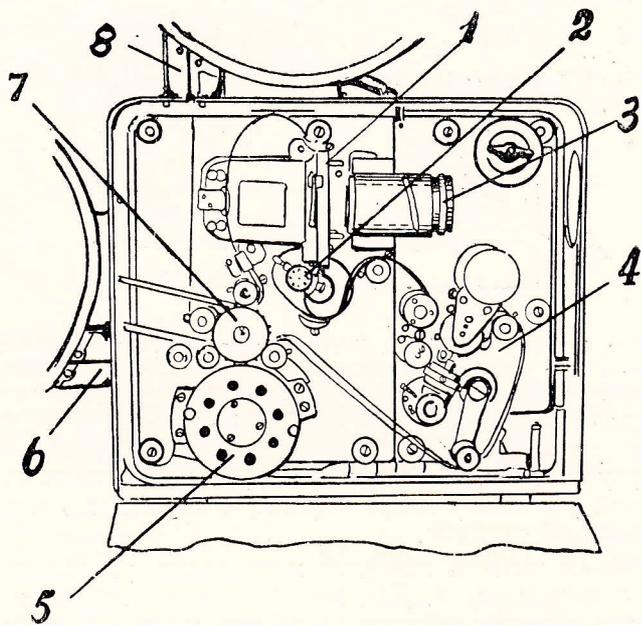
Проектор К-303. Вид спереди при открытой крышке.
